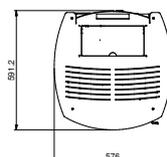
Dimensions générales: Mod.11kw extra-plat
